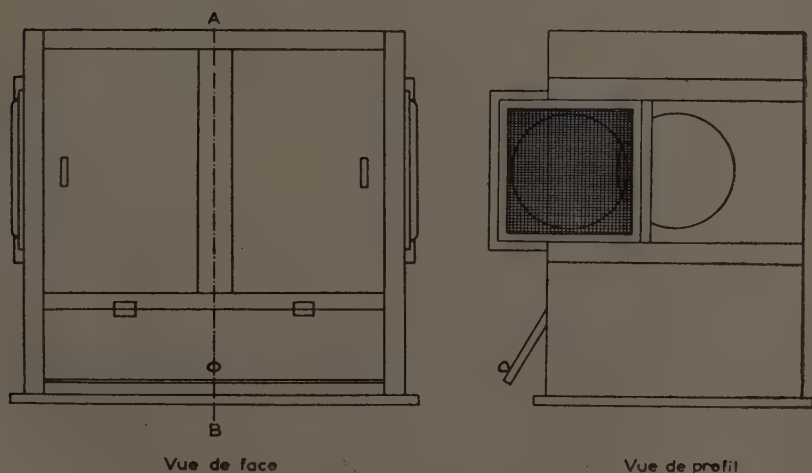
Cage de type « A » Dimensions utiles : 47 × 44 × 33 cm.
